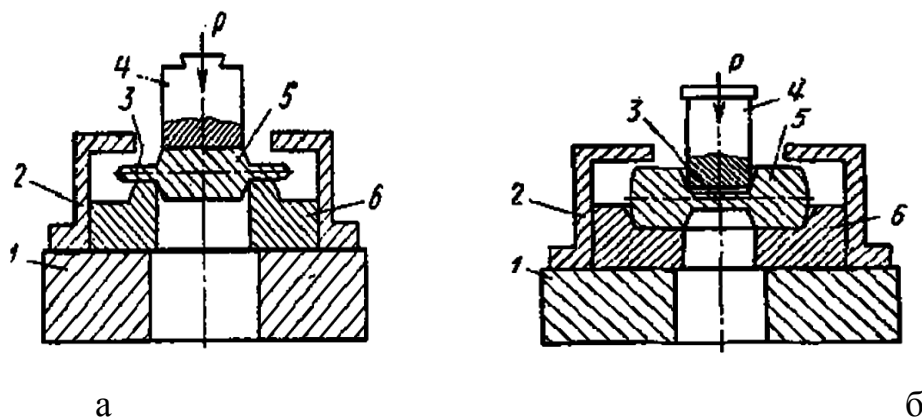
а – схема обрезного штампа, б – схема прошивного штампа;
